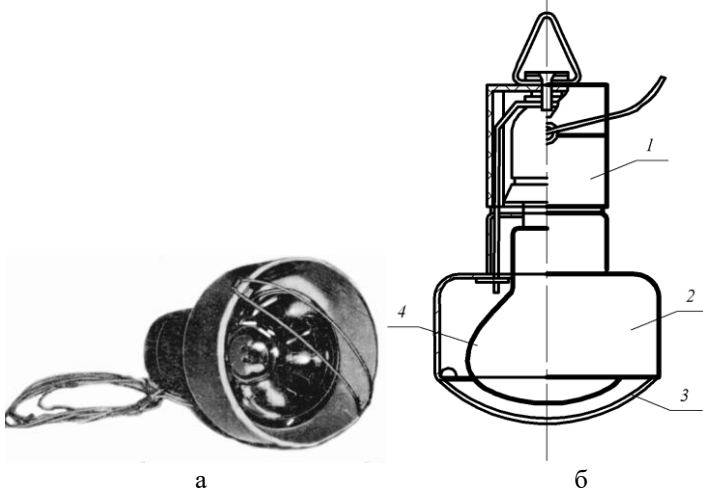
Опромінювач ветеринарний типу ОВИ-1: а) загальний вигляд; б) розріз: 1 – корпус; 2 – пластмасовий ковпак; 3 – захисна сітка; 4 – ІЧ-лампа
